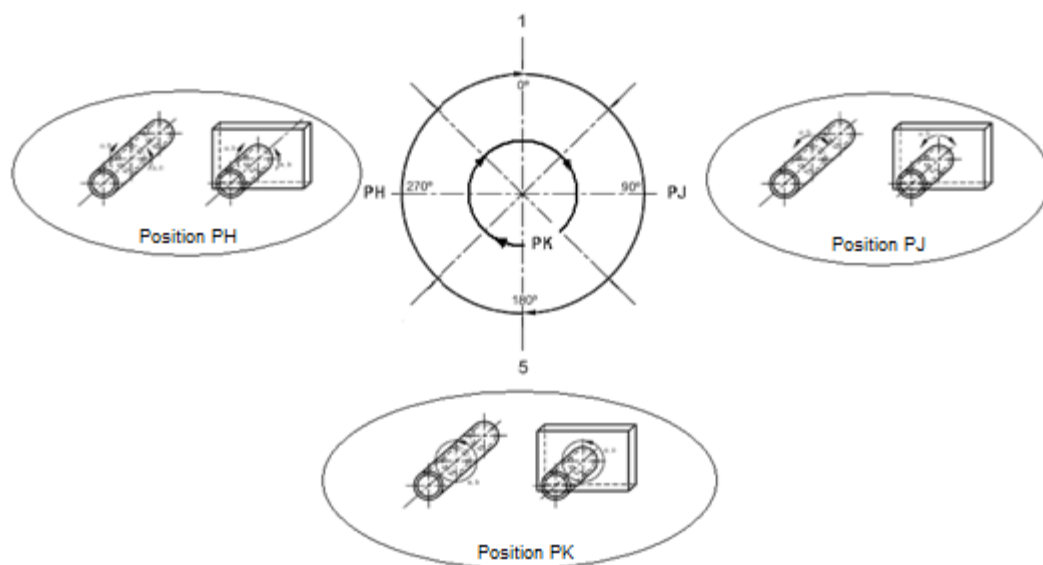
Principais Posições de Soldadura de Tubos.
